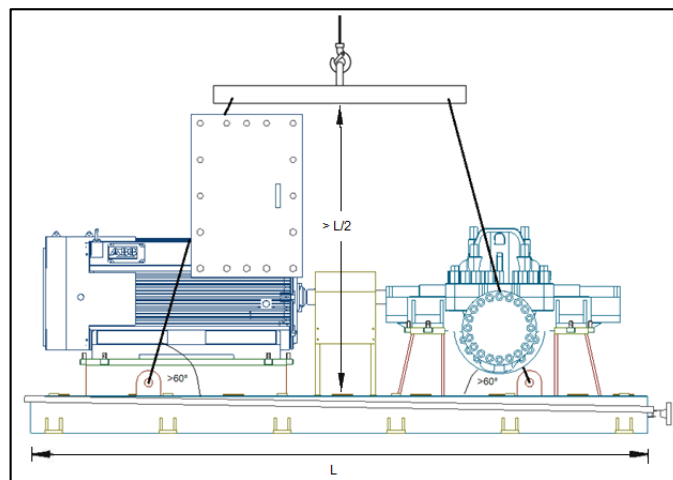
28 Izaje con barras de aducción (vista frontal)
